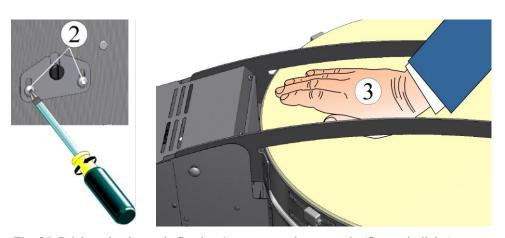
Dévisser la plaque de fixation / appuyer sur le couvercle (figure similaire)
